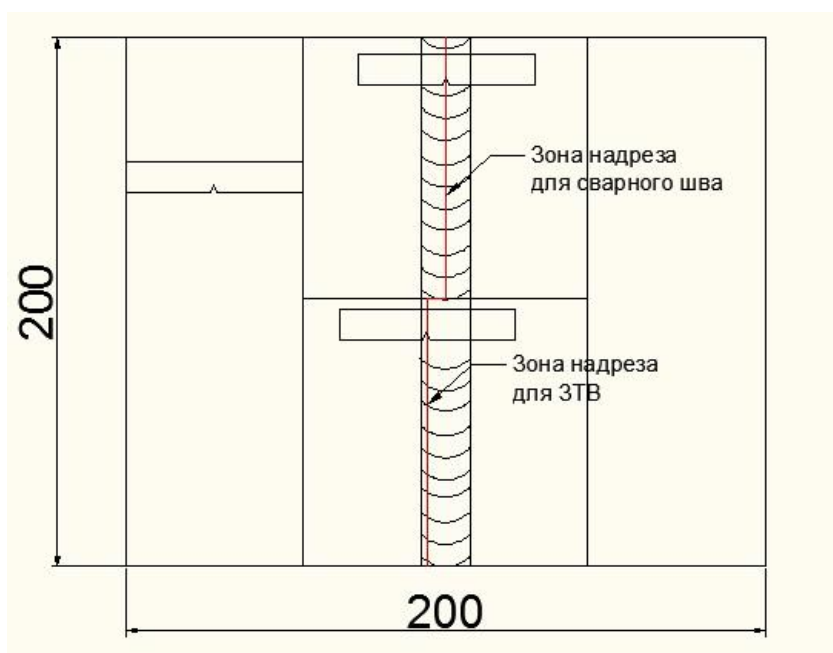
Схема вырезки образцов основного металла, металла шва и ЗТВ
